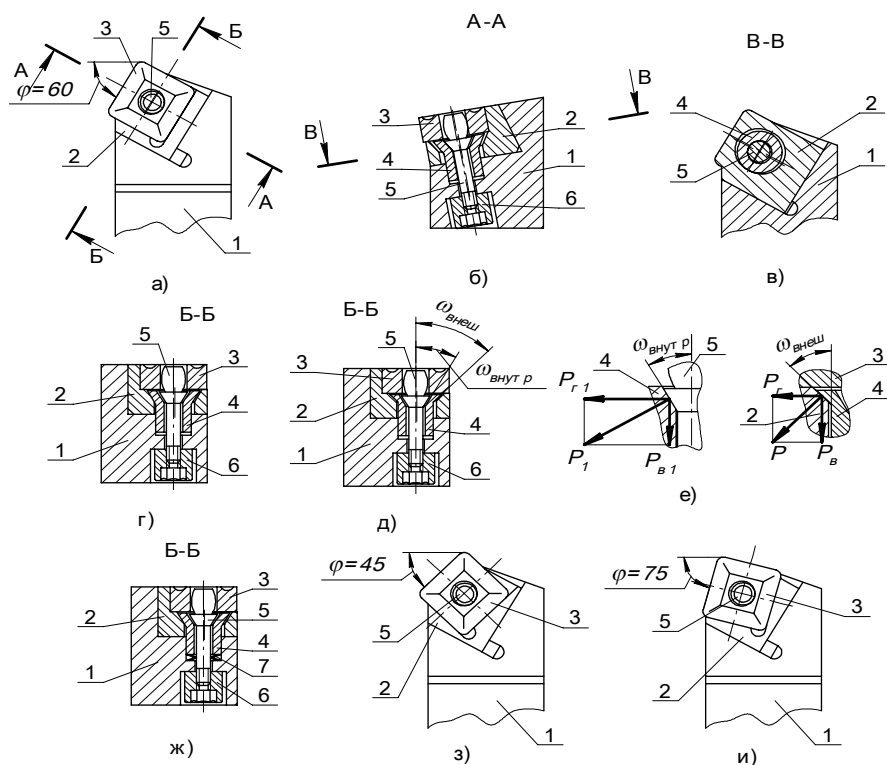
Универсально-сборный резец с повышенной надежностью крепления опорной подкладки с режущей
